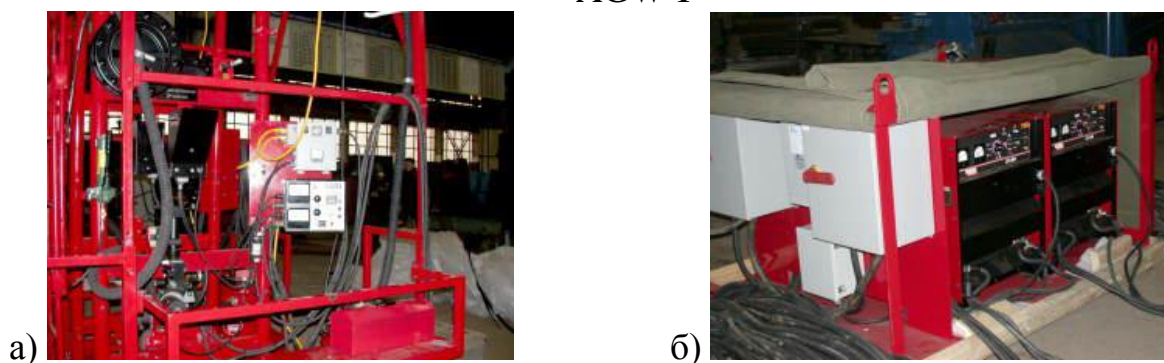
Комплектация сварочной установки AGW-I: головка NA-3 (а) и выпрямители DC-600 (б)
